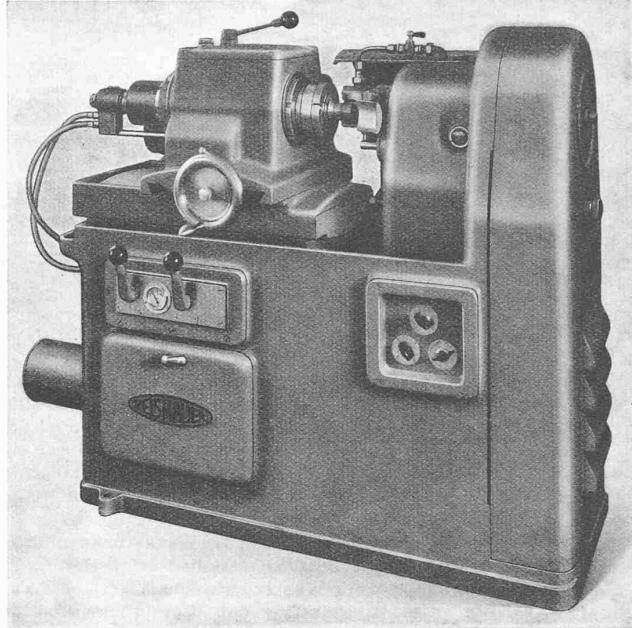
Hydraul. Kurzgewinde-Fräsmaschine Reishauer Typ KBH
